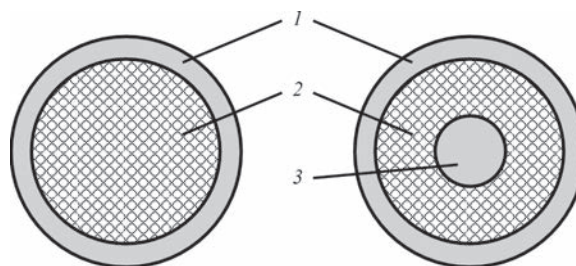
Поперечное сечение порошковой проволоки: 1 — оболочка; 2 — флюсовый наполнитель; 3 — сердечник
